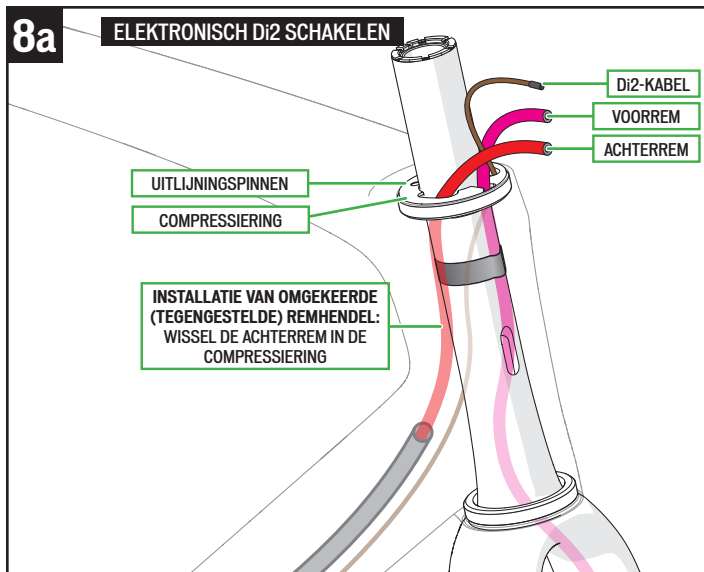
Installeer de compressiering (Elektronisch bekabelde schakelen).
